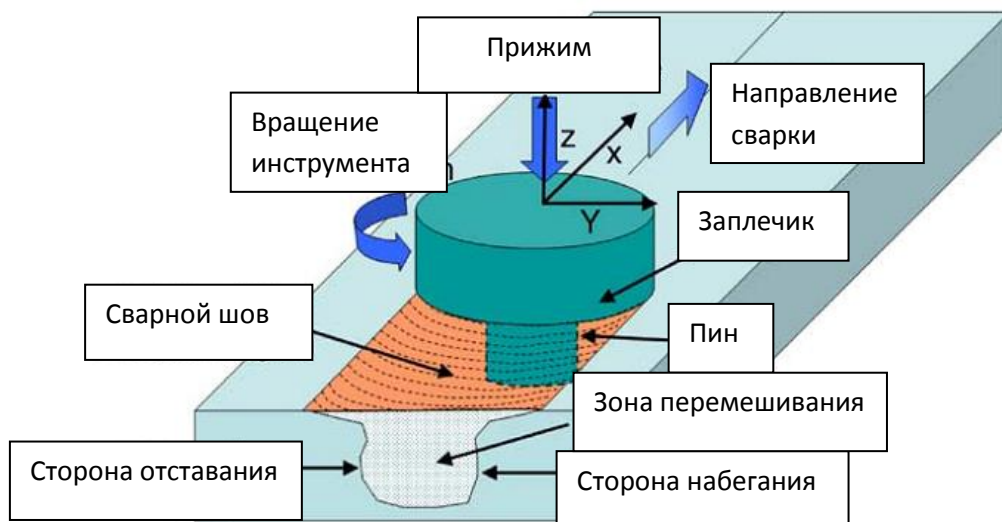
Схема процесса сварки трением с перемешиванием
